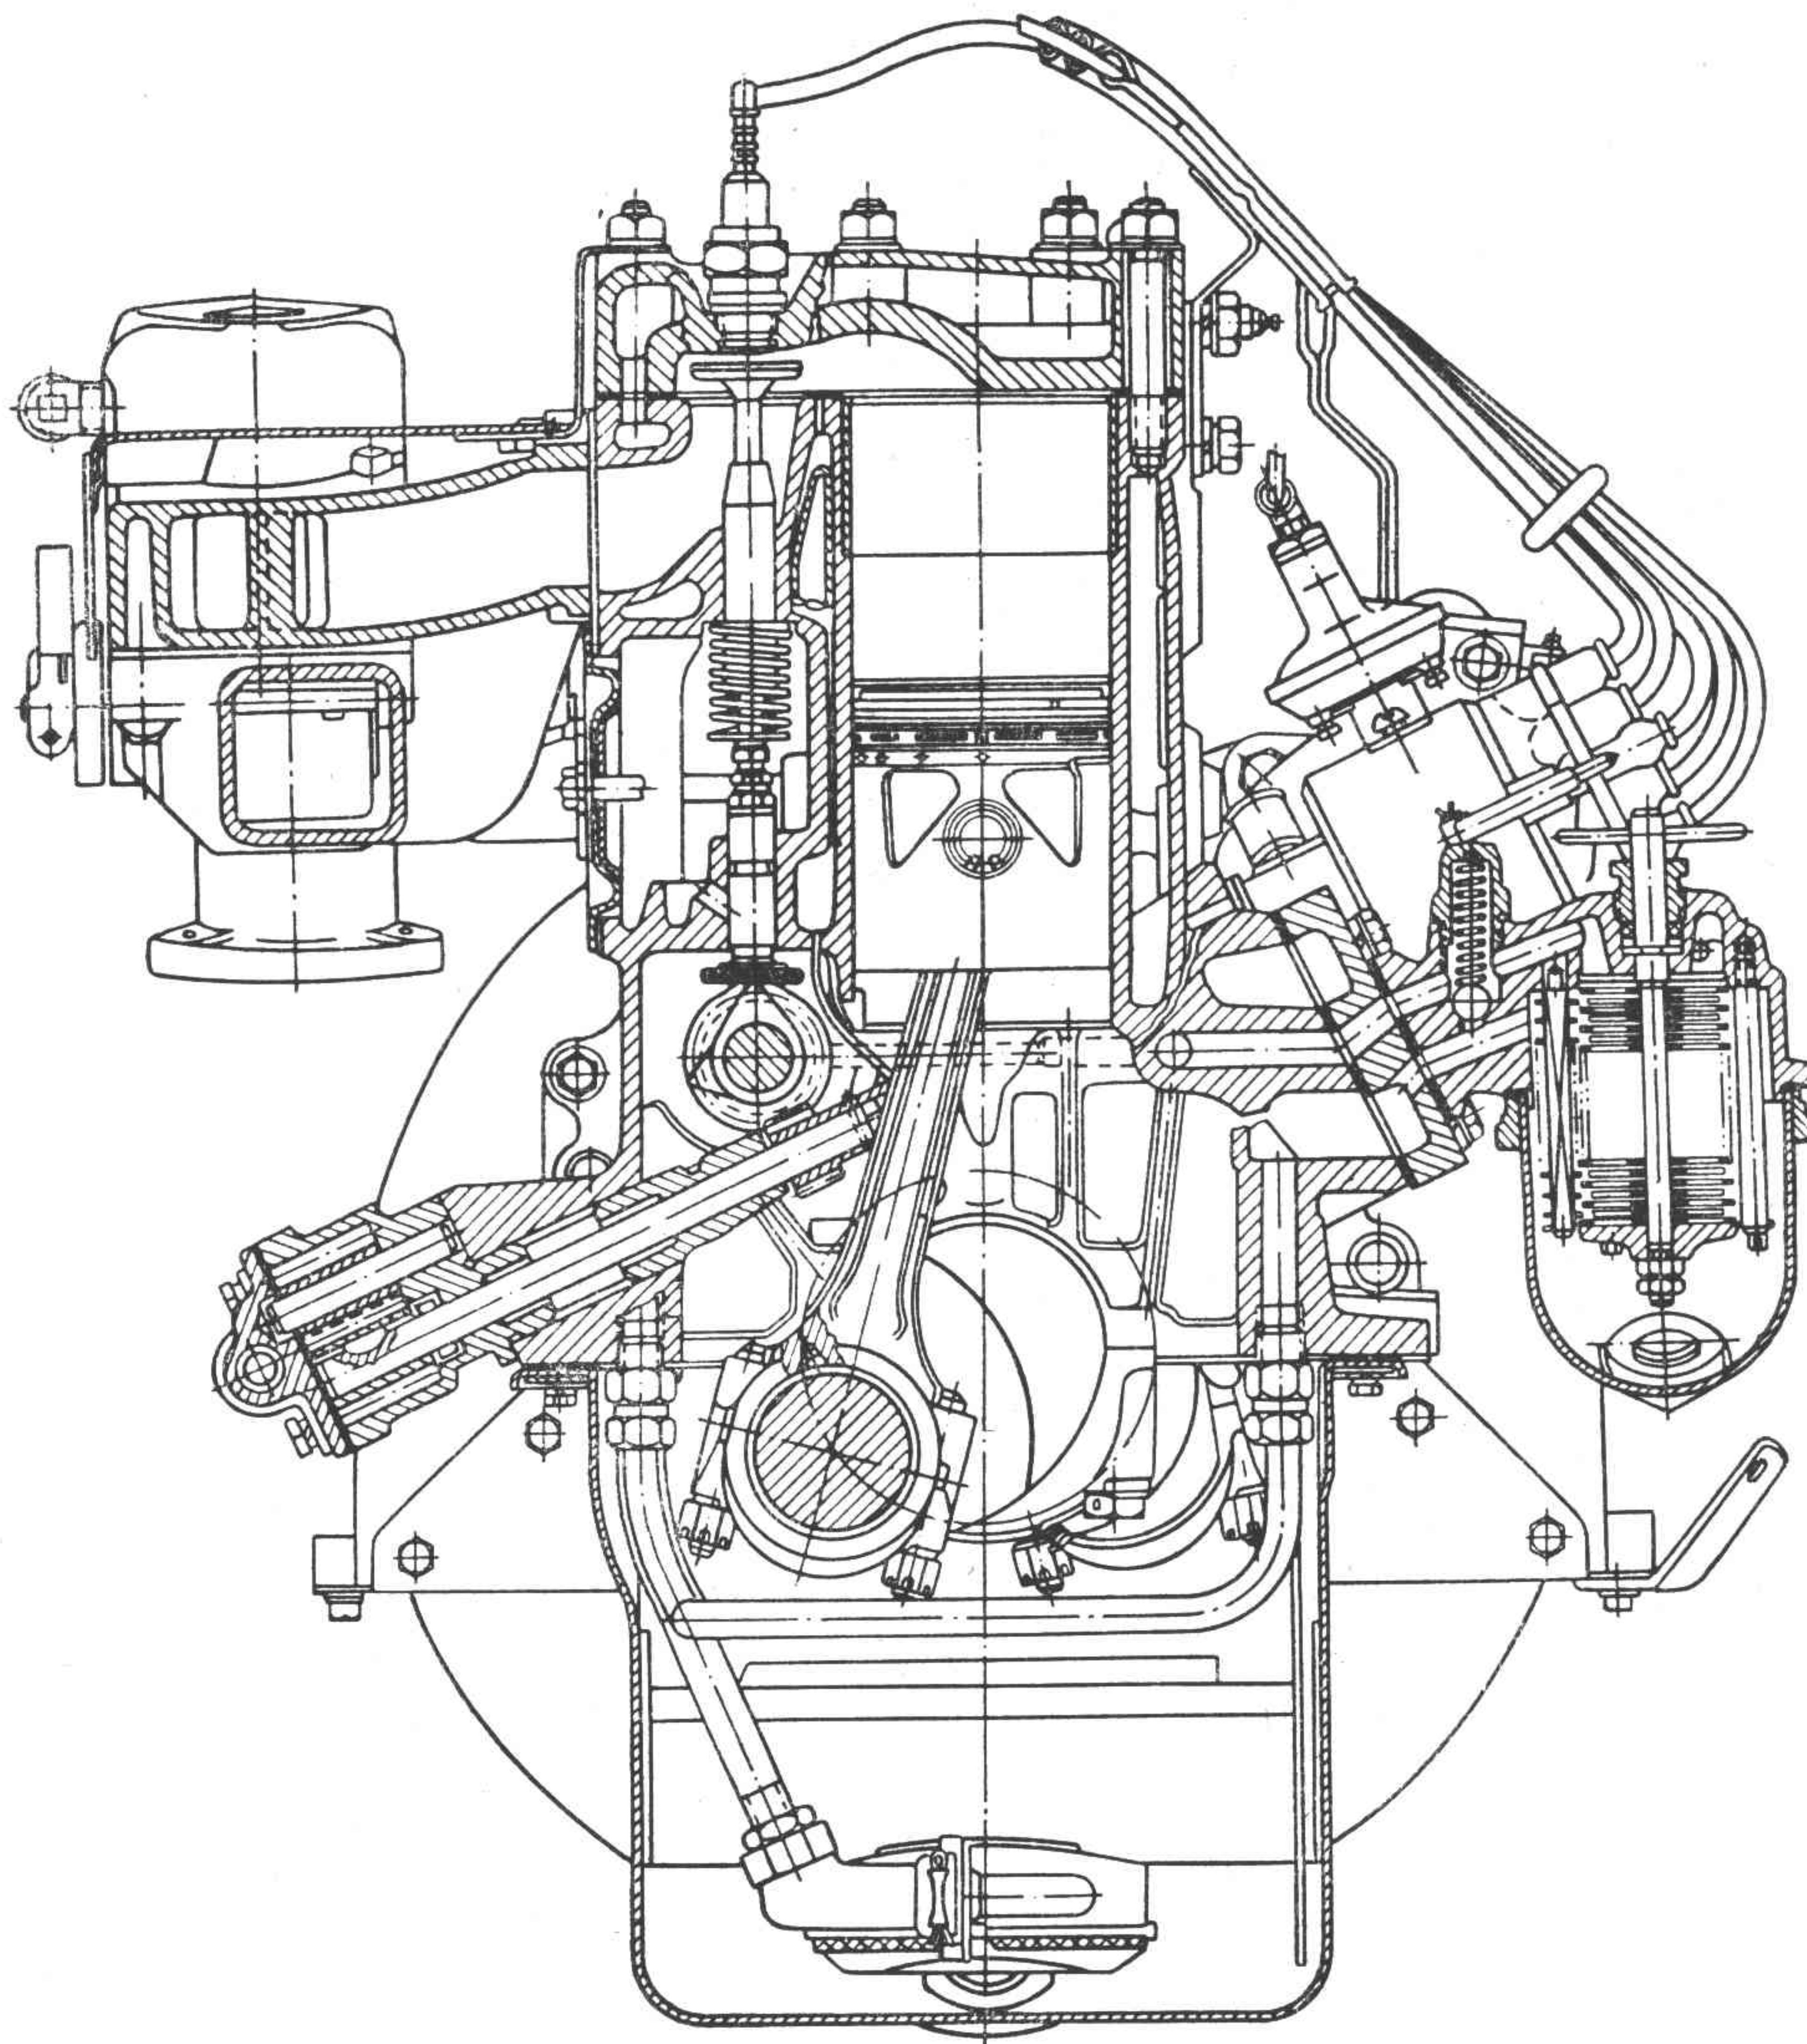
Поперечный разрез двигателя ГАЗ-51, ГАЗ-12
